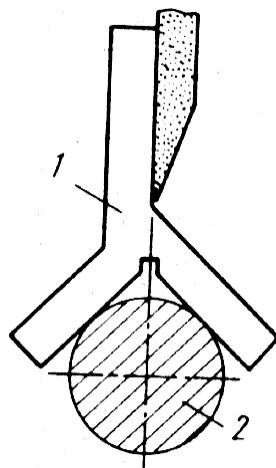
Установка шлифовального круга при формообразовании передней поверхности развертки:
